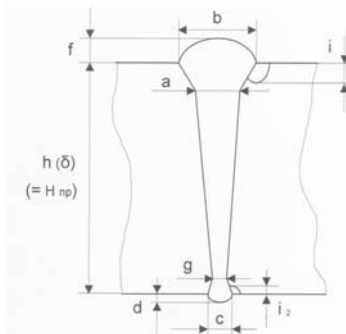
Сварной шов со сквозным проплавлением: H_{np} — глубина проплавления, равная толщине свариваемой пластины — $h(\delta)$; b, c — ширина лицевого и обратного валиков сварного шва; a — наибольшая ширина средней части зоны проплавления; g — наименьшая ширина средней части зоны проплавления; f, d — усиление лицевого и обратного валиков сварного шва; i_1, i_2 — величина подреза с лицевой и обратной стороны шва
